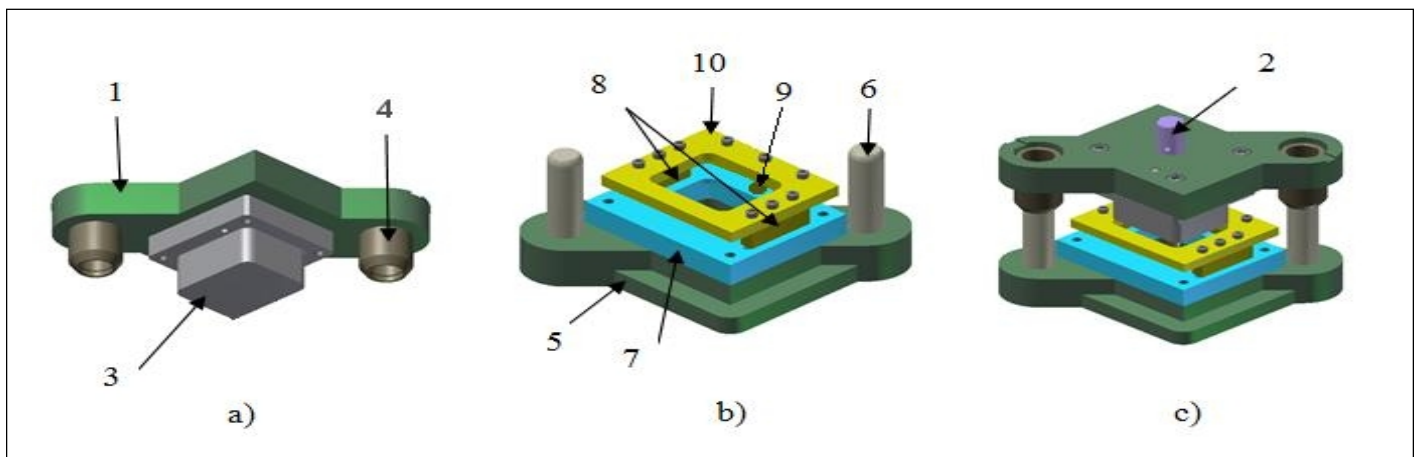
Troquel de corte: a) Conjunto superior; b) Conjunto inferior; c) Troquel completo
